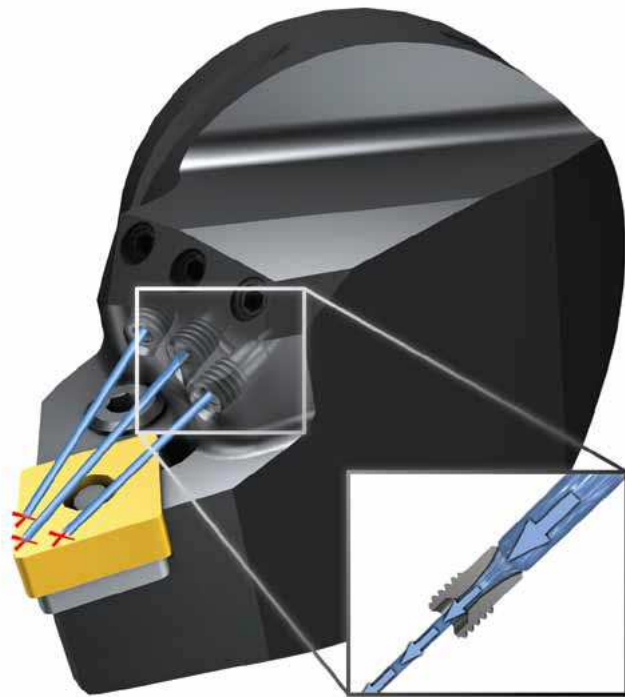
Produkt Jetstream Tooling od firmy SECO [22]
